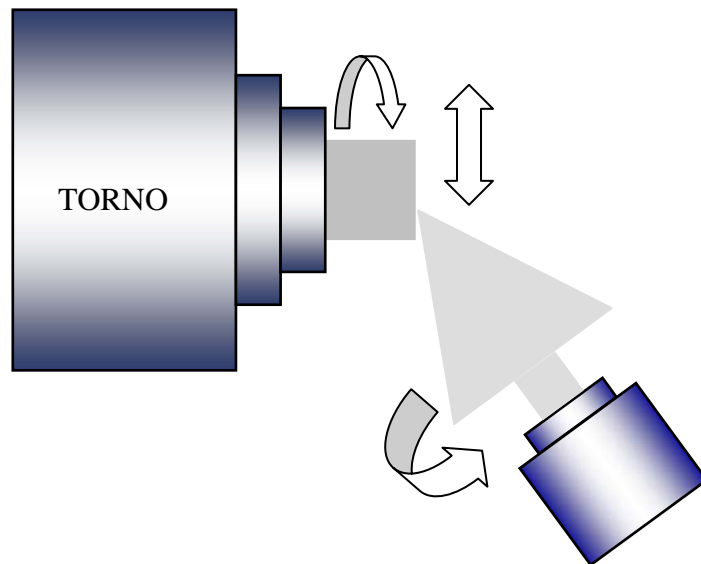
Desenho da deposição mecânica em corpos-de-prova cilíndricos.
